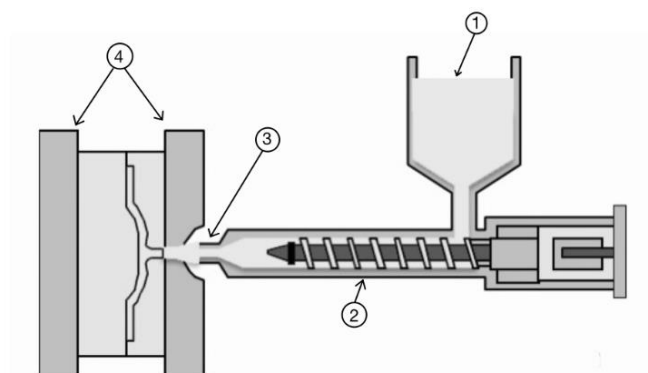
Partes principales máquina moldeo por inyección. Fuente: [122]
